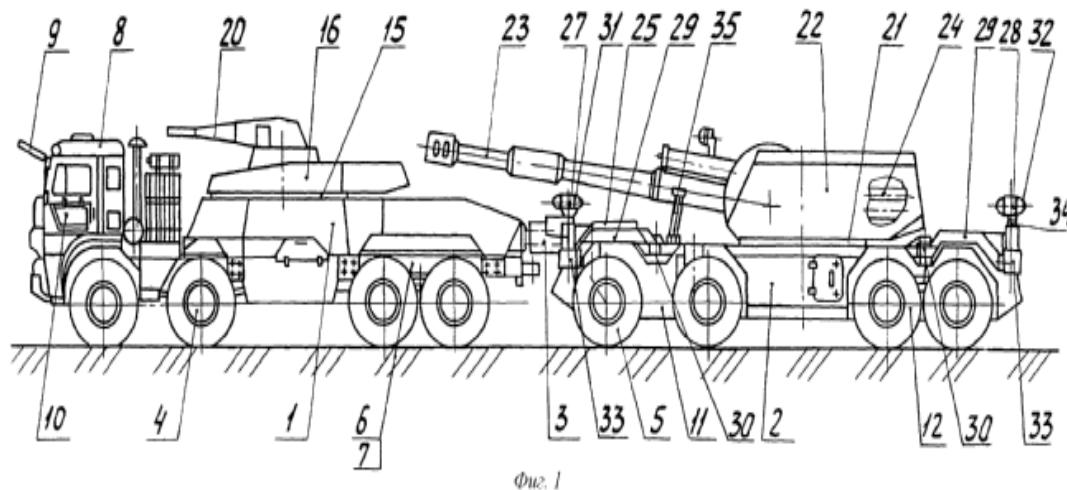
Самоходная артиллерийская сочлененная установка
